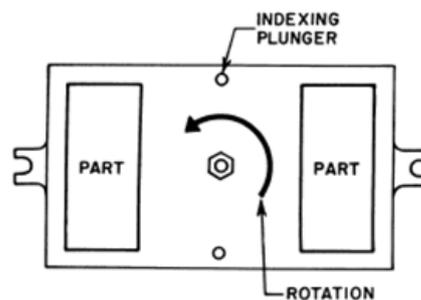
Benda Kerja Yang Di Mesin Dengan Fixture Index
